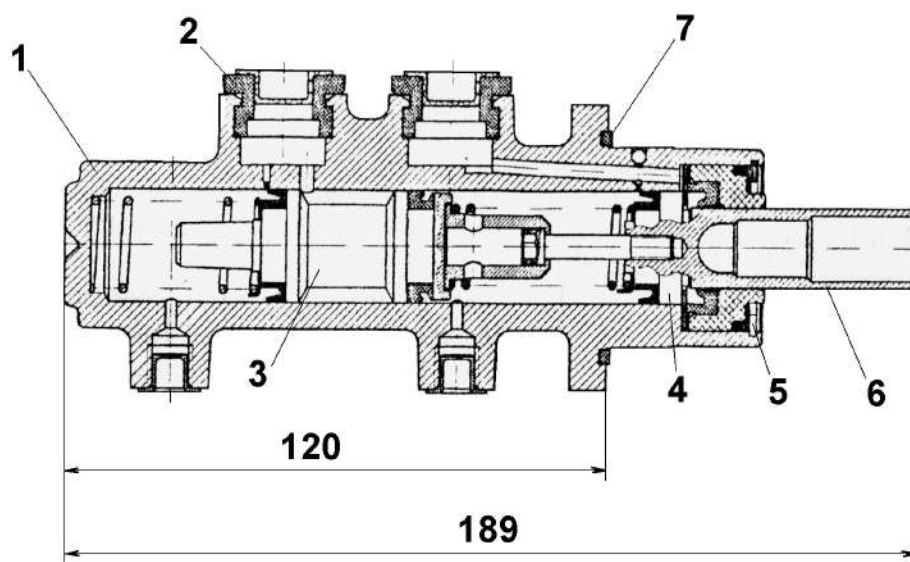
Главный тормозной цилиндр: 1- корпус; 2- резиновый уплотнитель бачка; 3, 4- поршни привода контуров; 5- распорное кольцо; 6- толкатель; 7- уплотнительное кольцо
